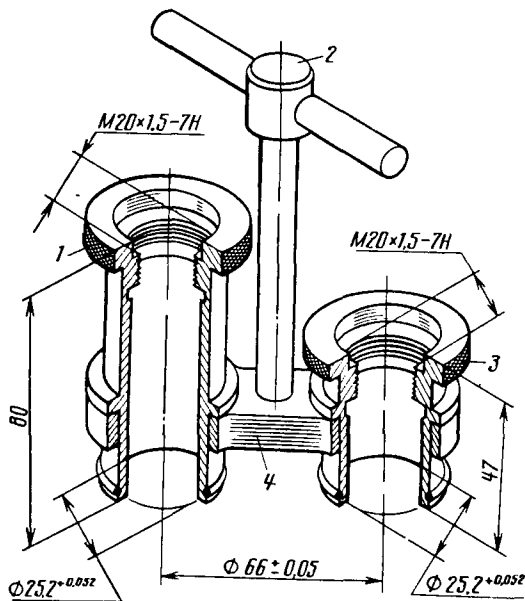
Приспособление для снятия и установки ведущего и ведомого валов коробки передач:
